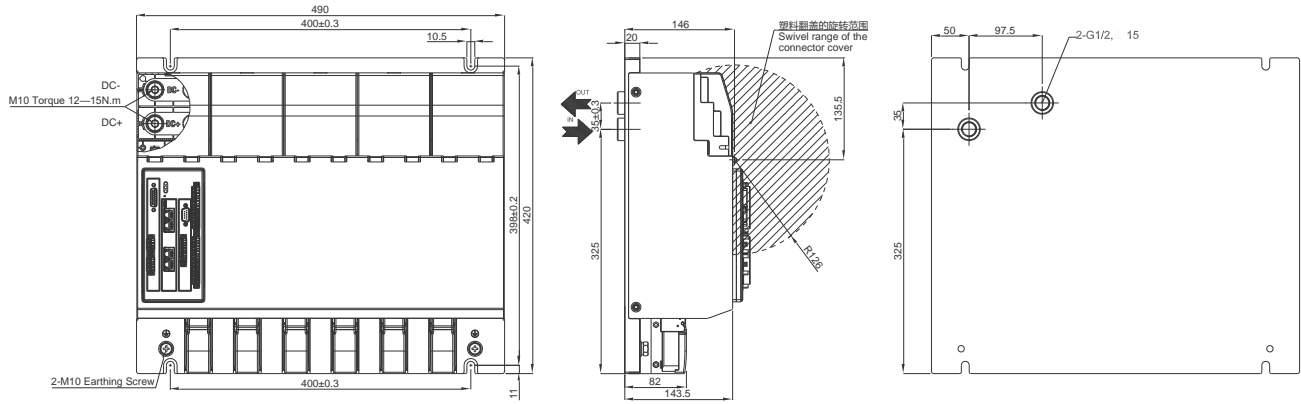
AxN-PS.080.4 冷却板安装 Cold plate mounting
